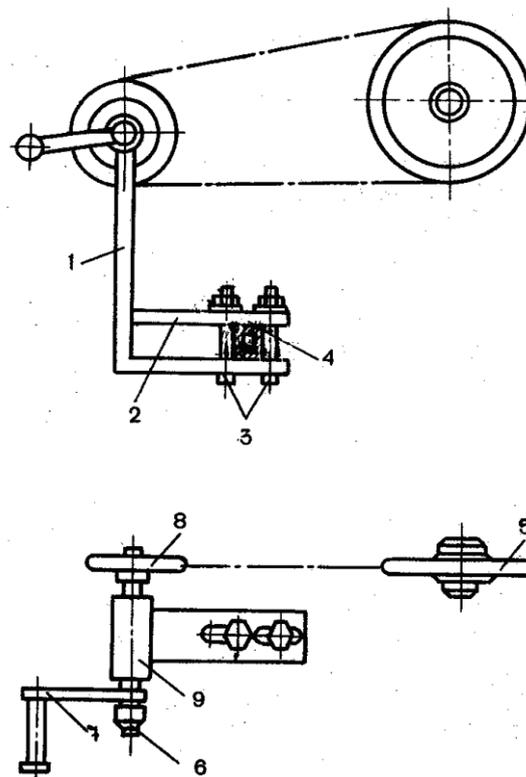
Приспособление для прокручивания вала высевяющих аппаратов сеялок: 1 — кронштейн; 2 — пластины; 3 — болты; 4 — рама сеялки; 5 — втулка; 6 — валик; 7 — рукоятка; 8, 9 — звездочки
